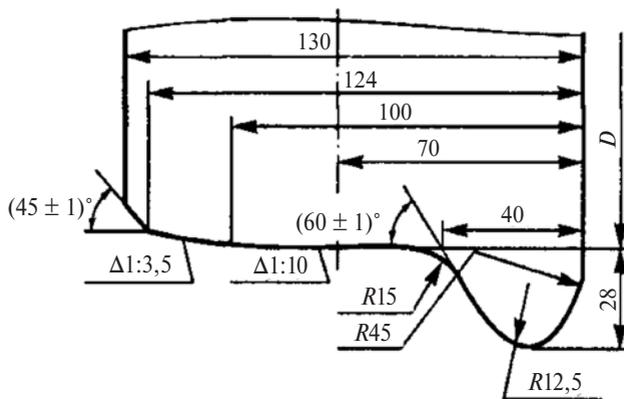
Стандартный профиль поверхности катания колес для вагонов
